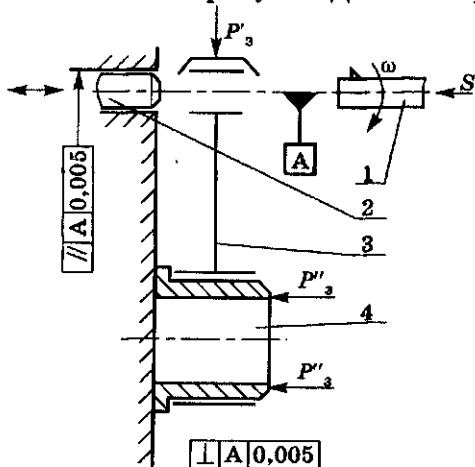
Схема установки и базирования шатуна при растачивании отверстия в верхней головке: 1 — шпиндель станка; 2 и 4 — оправки; 3 — деталь
